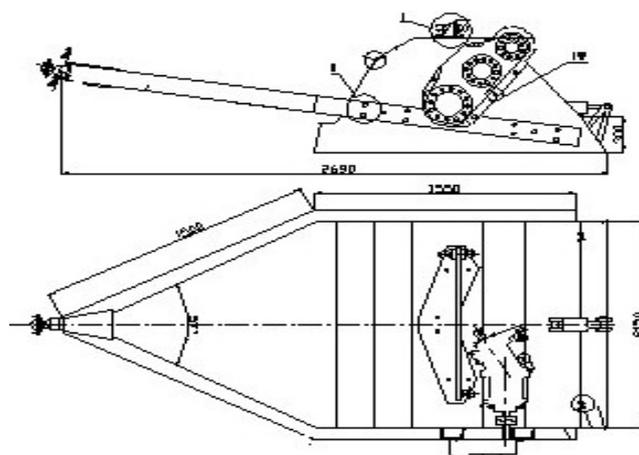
Навесное грунтосмесительное рабочее оборудование на автогрейдер ДЗ-180
